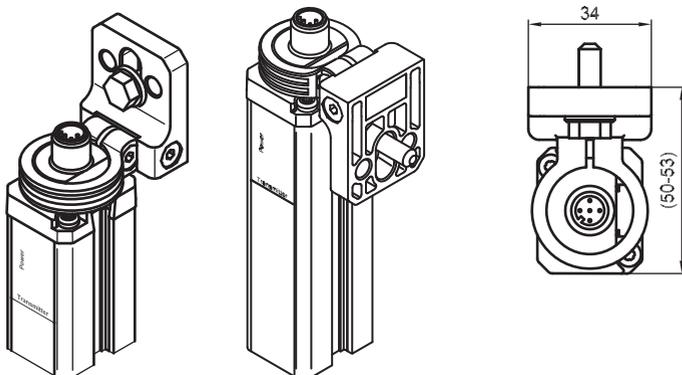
Halterung 360° drehbar, Montagebeispiele
